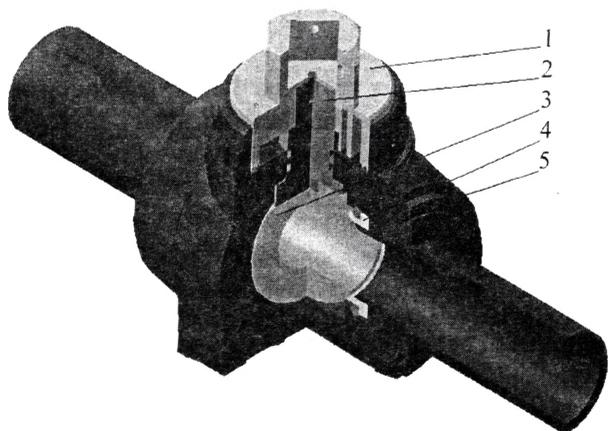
Шаровой кран: 1 — крышка, 2 — шток, 3 — полимерный шар, 4 — резиновое уплотнение, 5 — полиэтиленовый корпус
